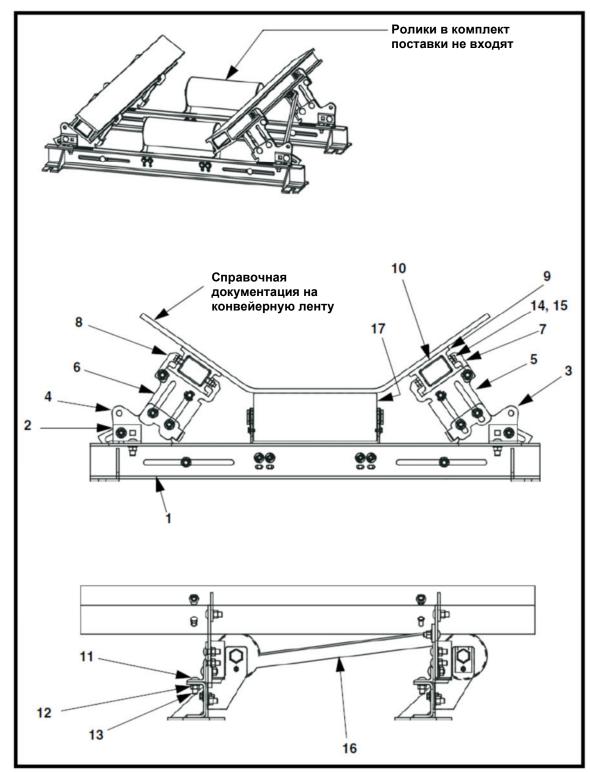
а. Сборка скользящей опоры Martin® (с одной балкой), номер детали 36700-XXX
